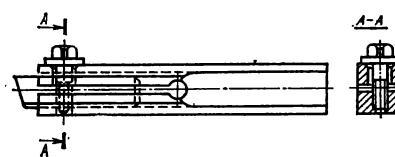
Приспособление для быстрого отвода резьбового резца
